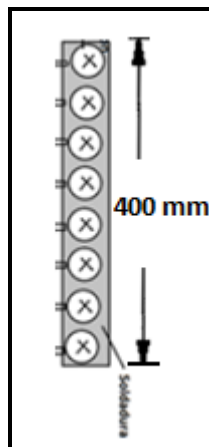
DIMENSIONAMIENTO DEL CORDÓN DE SOLDADURA EN LA PLACA INCLINDA Y LA CHAPA METÁLICA.
